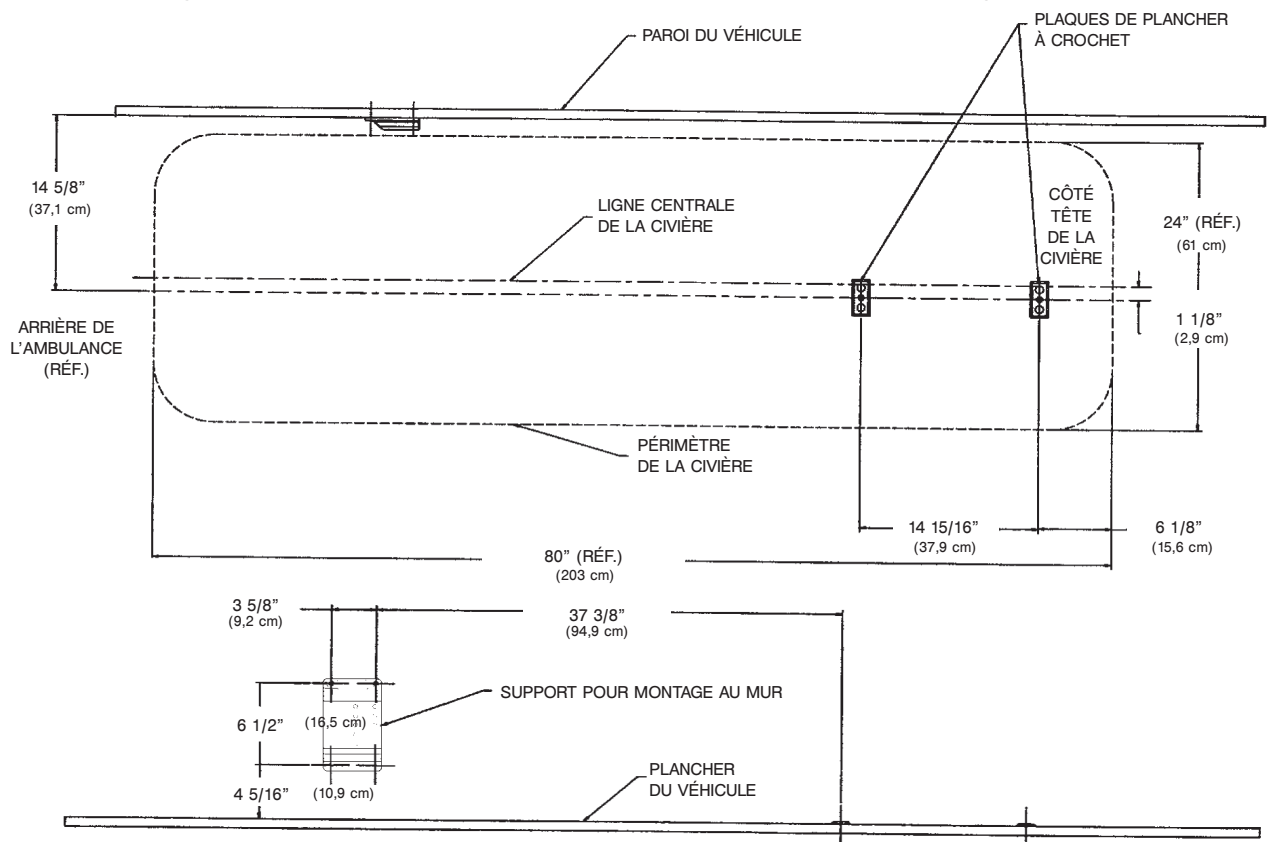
Spécifications d'installation – dispositif de fixation pour montage à la paroi
